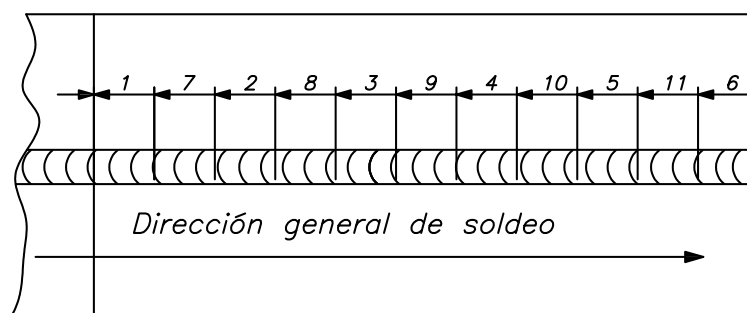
Soldadura a saltos en una junta a tope. (Masubushi, 1982)
